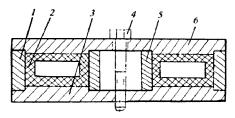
Установка резиновой камеры в металлическую форму для вулканизации:
